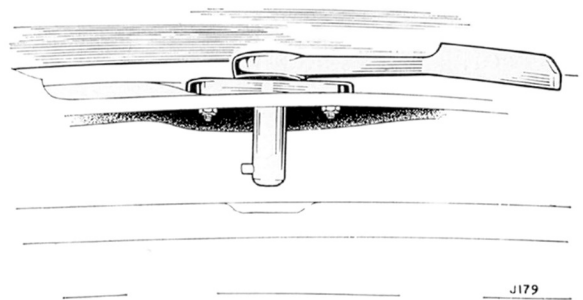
Levier de verrouillage (à partir du n° d'identification FD 20001 en conduite à gauche et FD 15701 en conduite à droite)
